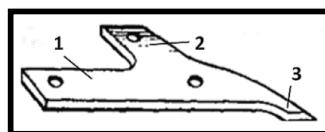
Лемех вырезной: 1 – лемех; 3 – щиток; 3 – долотообразный носок.
